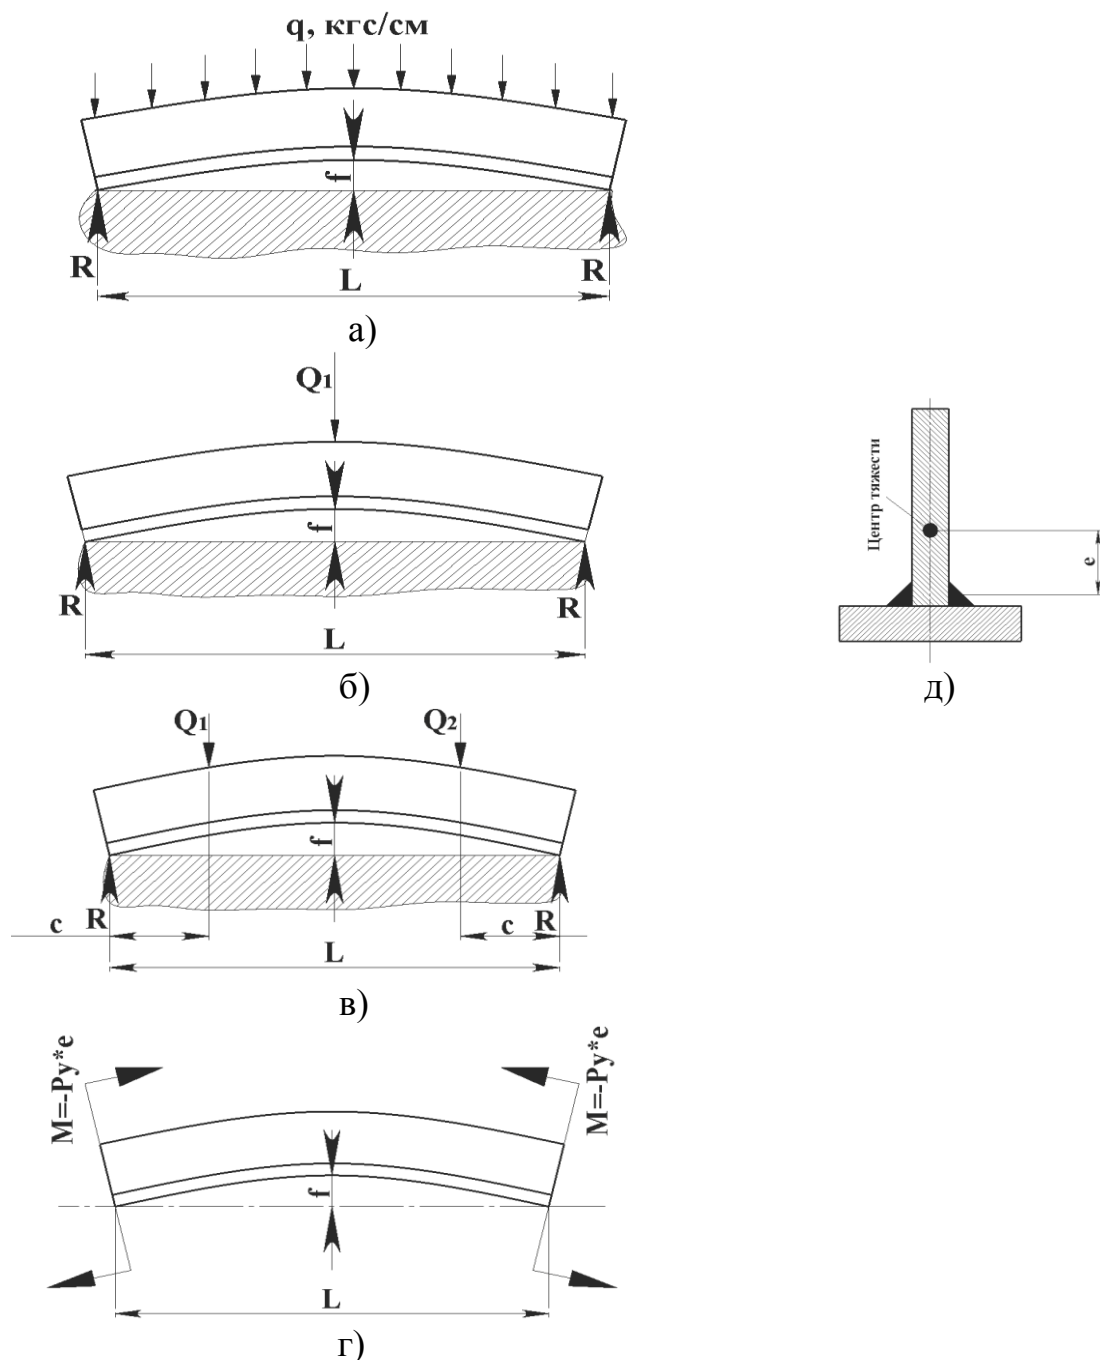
Продольная деформация сварной балки и схемы ее нагружения в сборочно–сварочном кондукторе:
